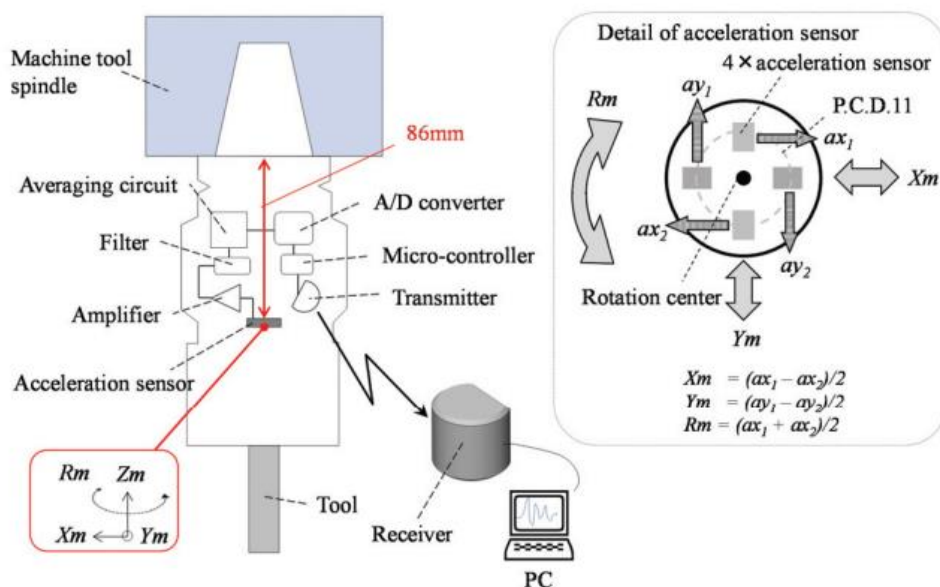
Схема бездротового вимірювання вібрацій у патроні для осьових інструментів [22]
